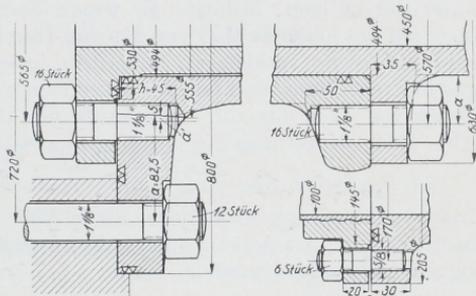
bis 1758. Flanschverbindungen am Zylinder Abb. 1755. M. 1:5. Abb. 1756. Anschluß am Rahmen und Verschraubung des vorderen Deckels. Abb. 1757. Verschraubung der Köpfe mit dem Laufzylinder. Abb. 1758. Anschluß des Zuleitungsrohres.
